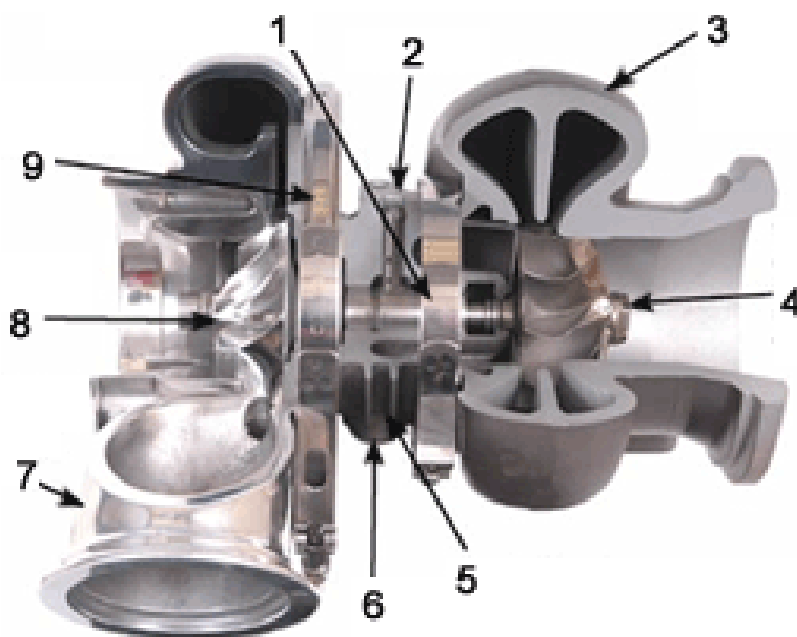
Turbo-compressor em corte (Fonte: Garrett)
